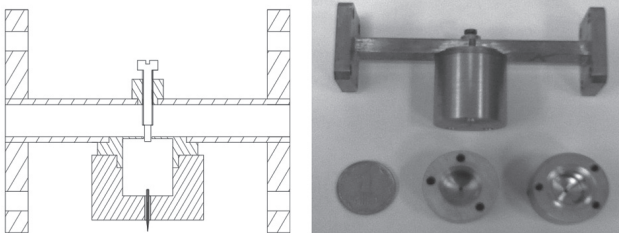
Типовая конструкция и внешний вид РИП на основе цилиндрического резонатора, возбуждаемого на типе колебаний E_{01n}
